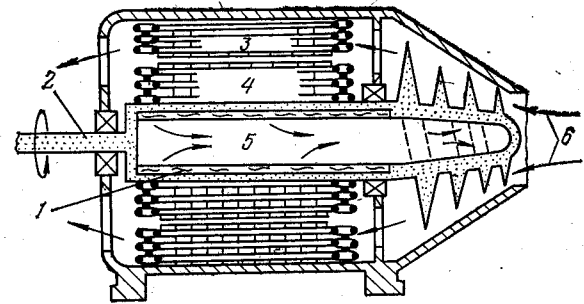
Асинхронный двигатель: 1 — жидкость; 2 — вращающийся вал; 3 — статор; 4 — ротор; 5 — пар; 6 — воздух
